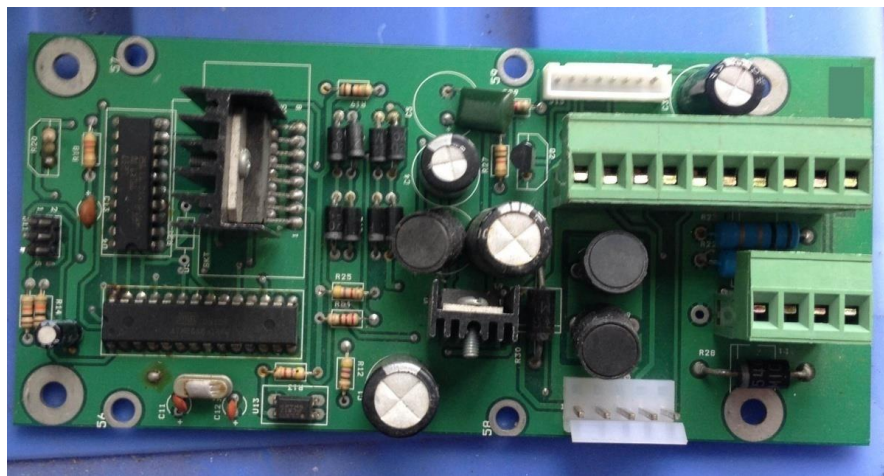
Общий вид изготовленного Репитера гирокомпаса
